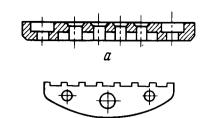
Детали клапанов: a — розетка всасывающего клапана компрессора АУ45;  $\delta$  — ограничитель клапана компрессора АУ200
